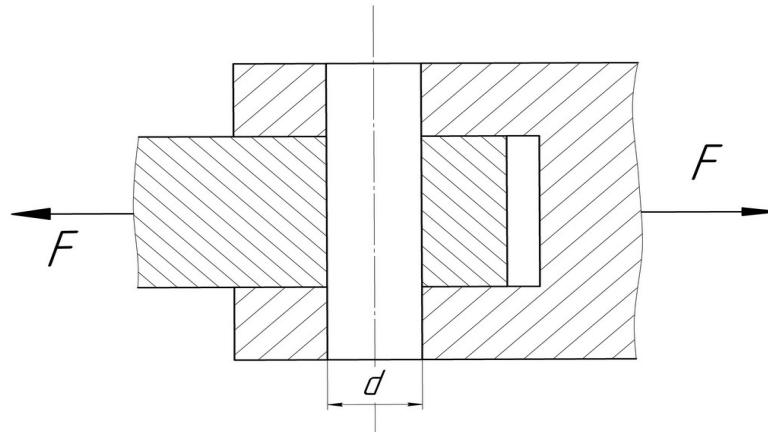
Розрахункова схема кріплення пальця гідроциліндра до порталу
